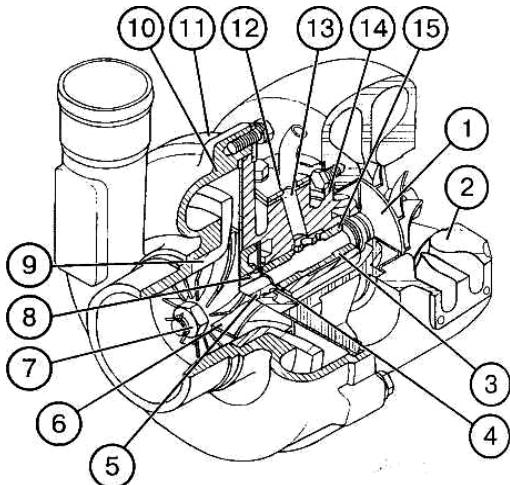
Турбокомпрессор: 1 — колесо турбины с валом; 2 — корпус турбины; 3 — подшипник; 4 — маслоотражатель; 5 — кольцо уплотнительное; 6 — колесо компрессора; 7 — гайка специальная; 8 — втулка; 9 — диффузор; 10 — диск; 11 — корпус компрессора; 12 — кольцо стопорное; 13 — фиксатор; 14 — корпус средний; 15 — втулка
